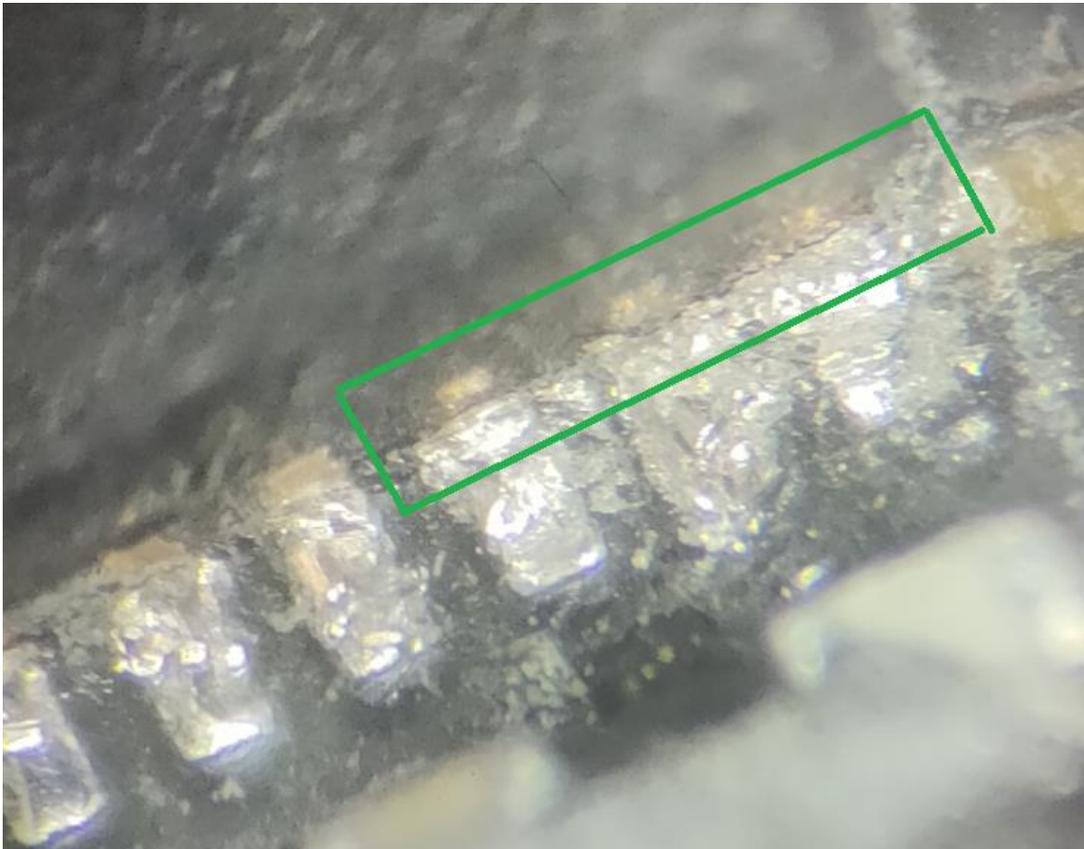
芯片的管脚和 PCB 板的焊盘存在裂缝
